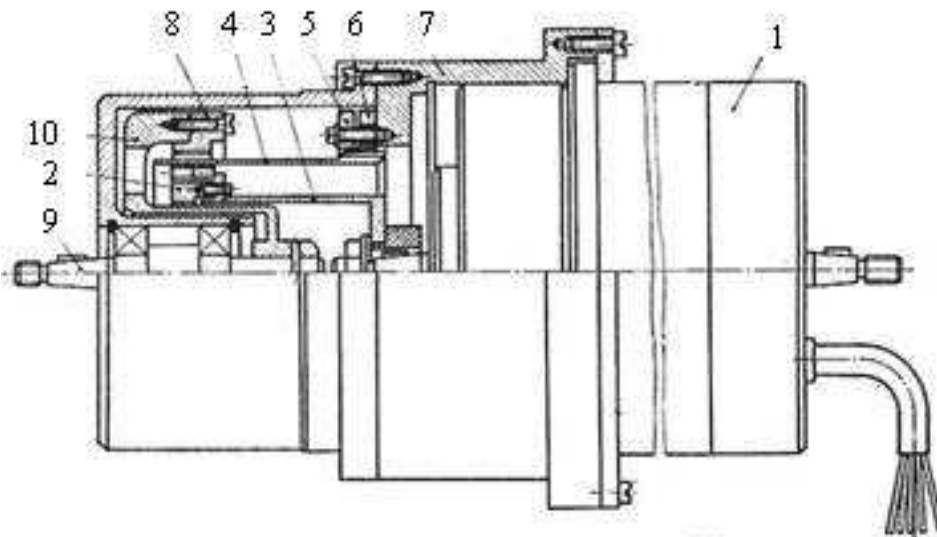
Motoreductor armonic cu motor pas cu pas
